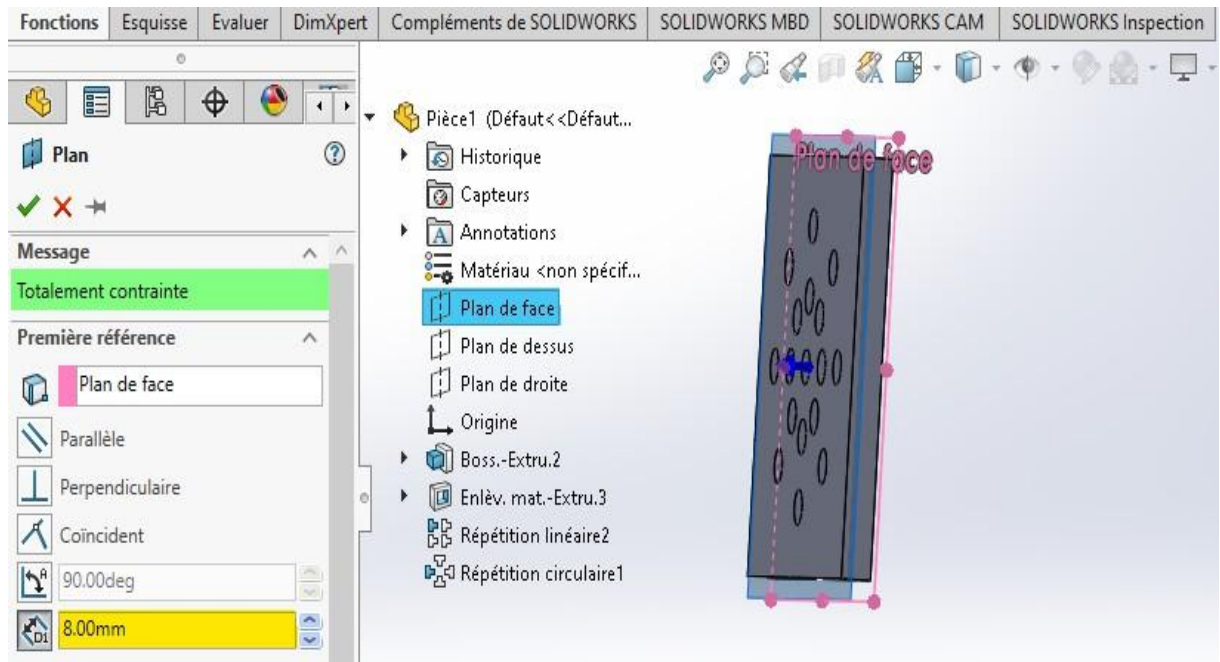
37 : Création du nouveau plan parallèle au plan de face
